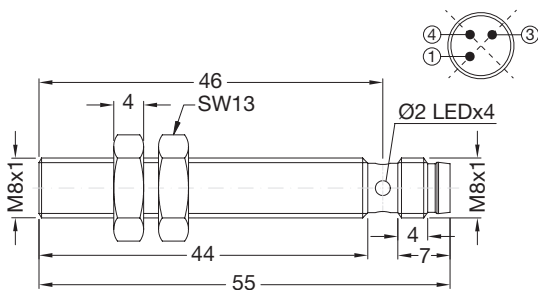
Lange Ausführung, bündiger Einbau, Steckversion
